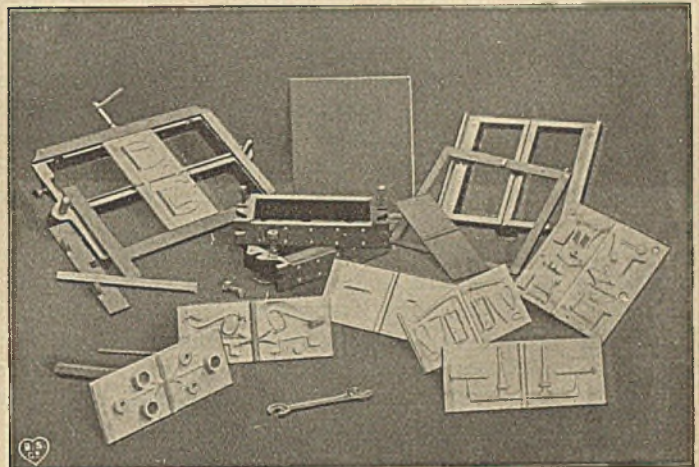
Klischeewerkzeug mit einigen Klischeeplatten und einem Einspannrahmen hierfür zum Gebrauch auf Formmaschinen.
